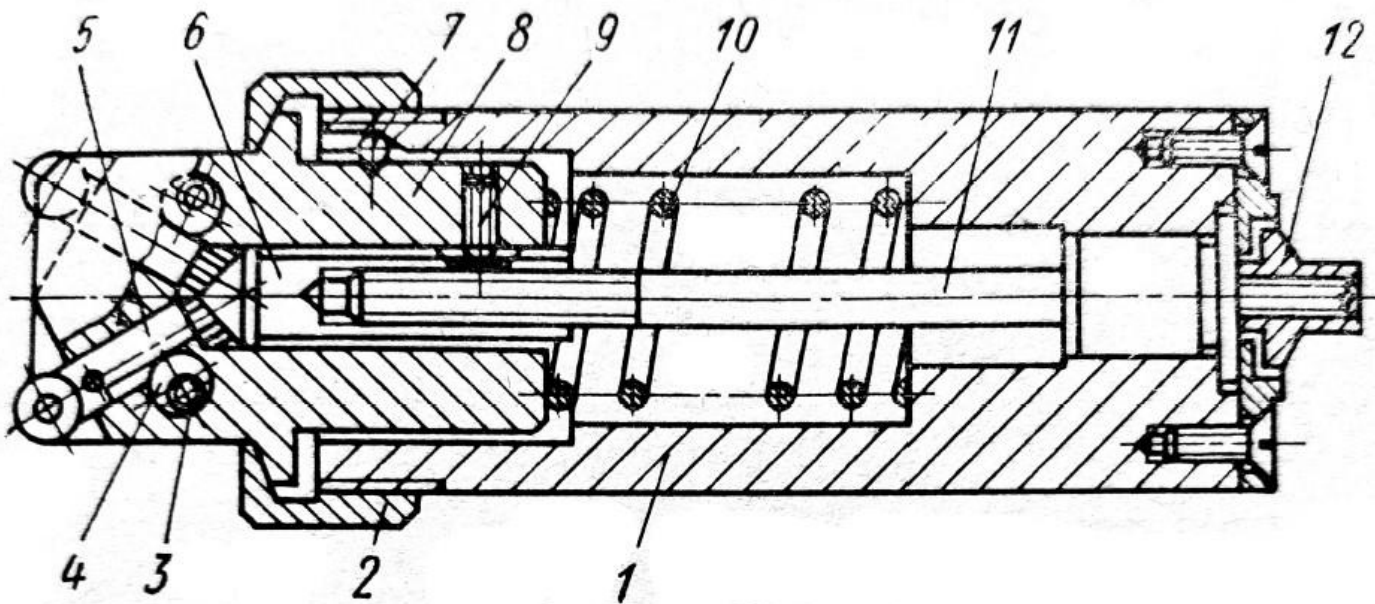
Варіант дволезової гойдальної розвертки із твердосплавними круглими пластинами
